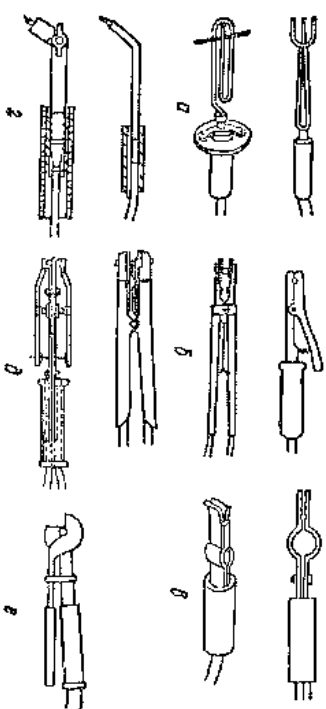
Конструктивные схемы электрододержателей для ручной дуговой сварки:
